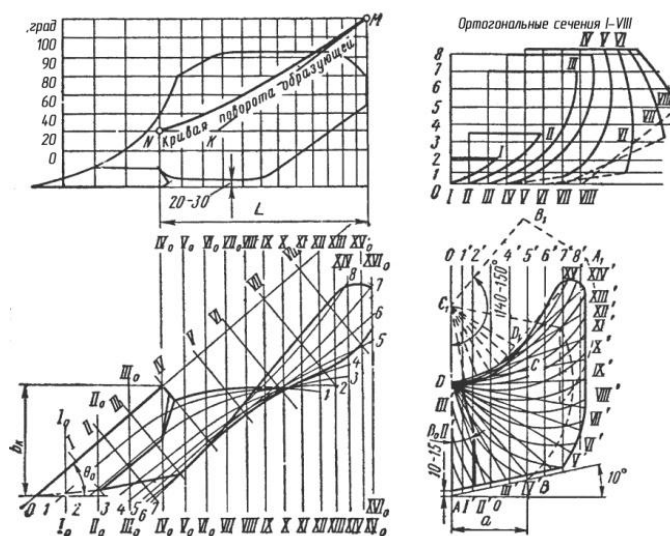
Гвинтовий тип корпусу відвального плуга
